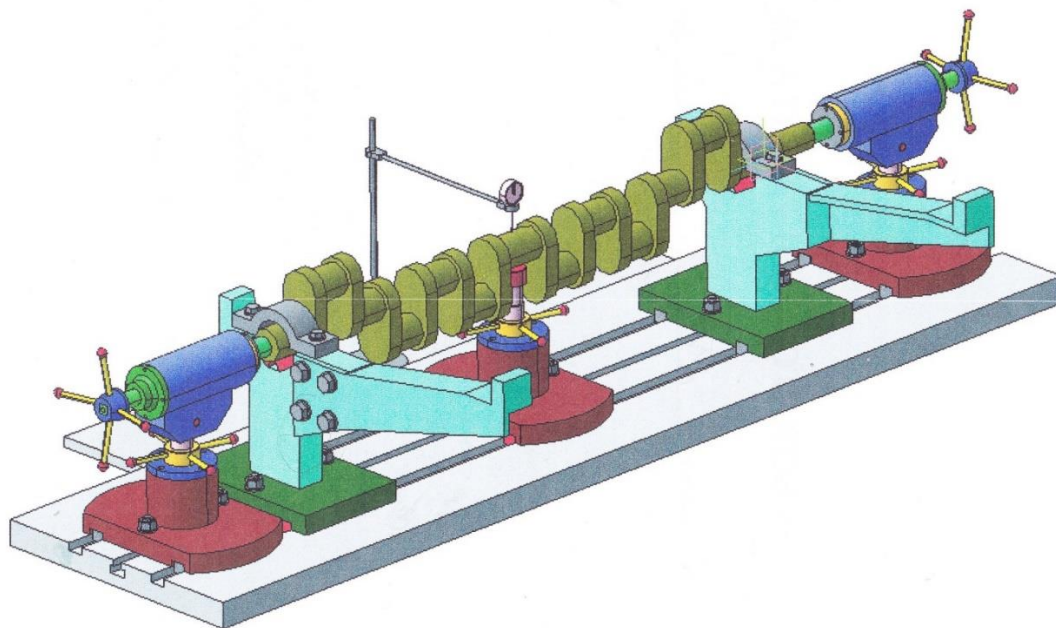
Новое устройство для проверки изгиба вала на центрах и выпрямления на гидравлическом прессе, 3D-модель;
